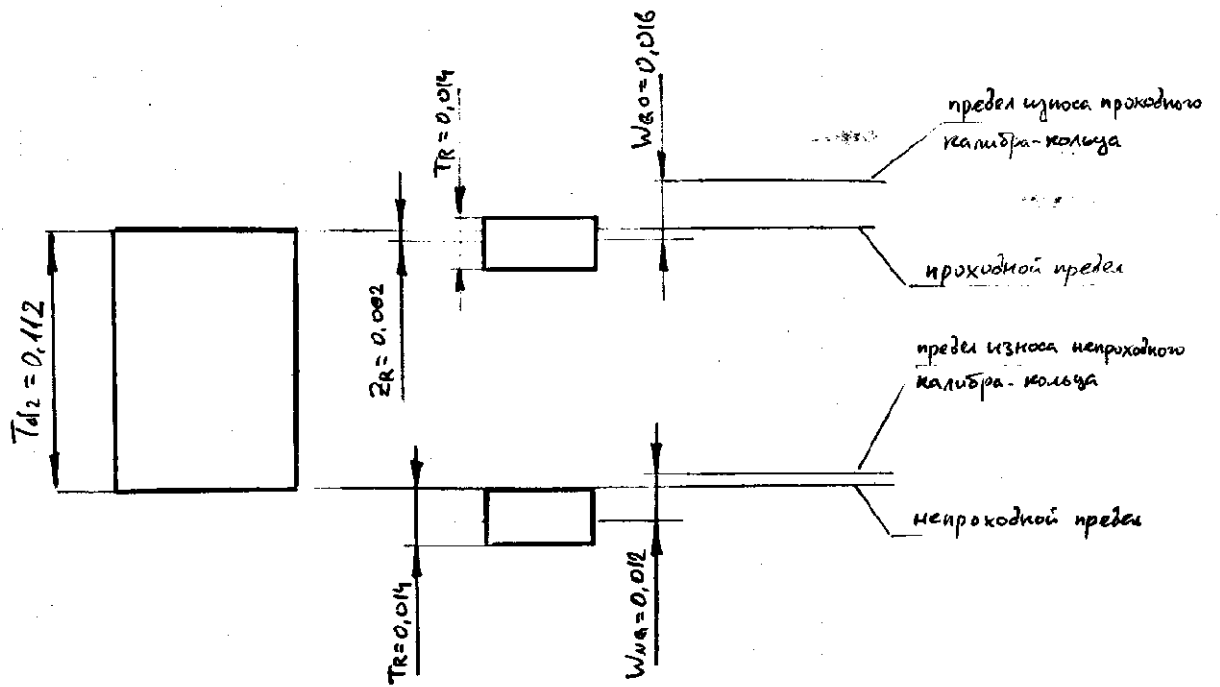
Расположение полей допусков среднего диаметра калибров для контроля наружной резьбы
